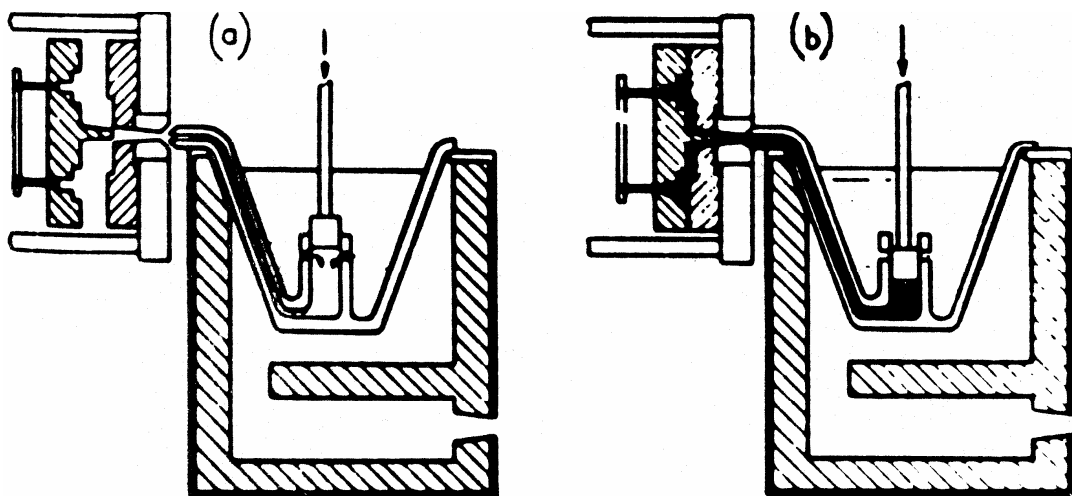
Equipamento de fundição de câmara fria em matriz, operado por pistão (equipamento de tubo curvado): (a) molde aberto antes da injeção do metal; (b) pistão operando para a injeção de metal no molde.
